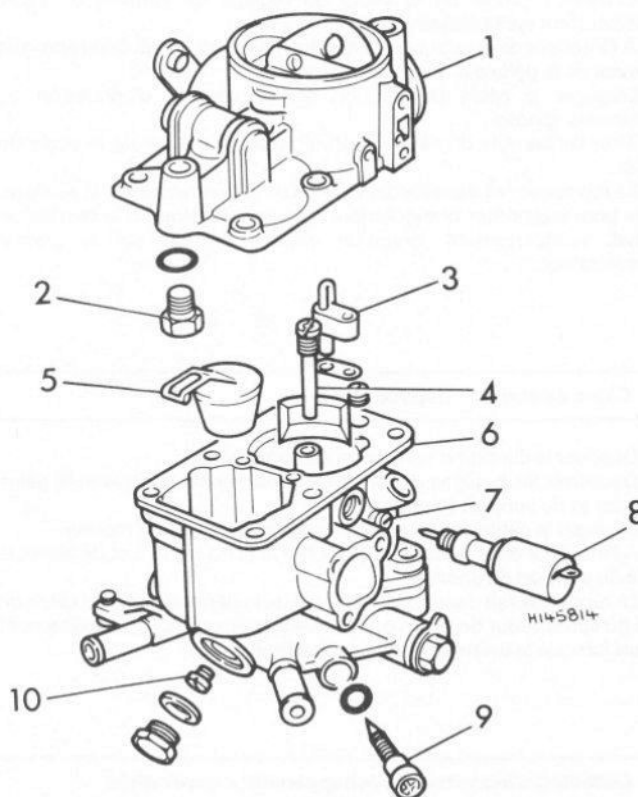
Eclaté du carburateur Solex 34 PBISA
